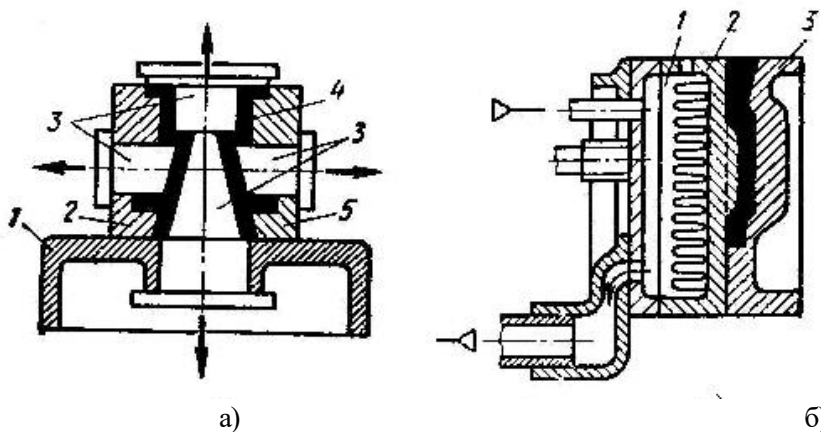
Конструкции кокилей: а) разъемного со стержнями: 1 – плита основания кокиля, 2 – левая полуформа, 3 – металлические стержни, 4 – отливка, 5 – правая полуформа; б) с водяным охлаждением левой полуформы: 1 – полость в левой полуформе для подачи в нее воды, 2 – левая полуформа, 3 – правая полуформа
